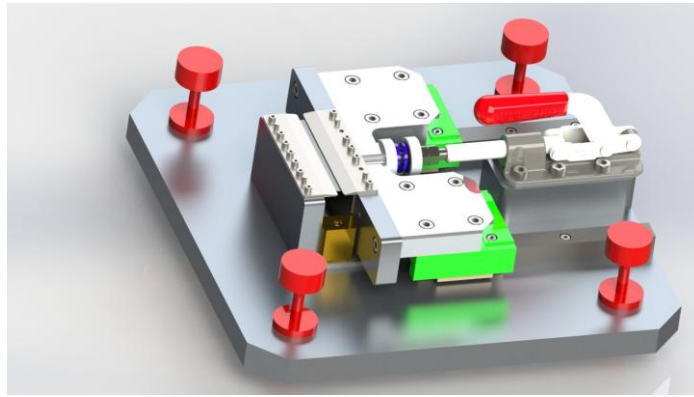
Utillaje de soldadura láser de virola
